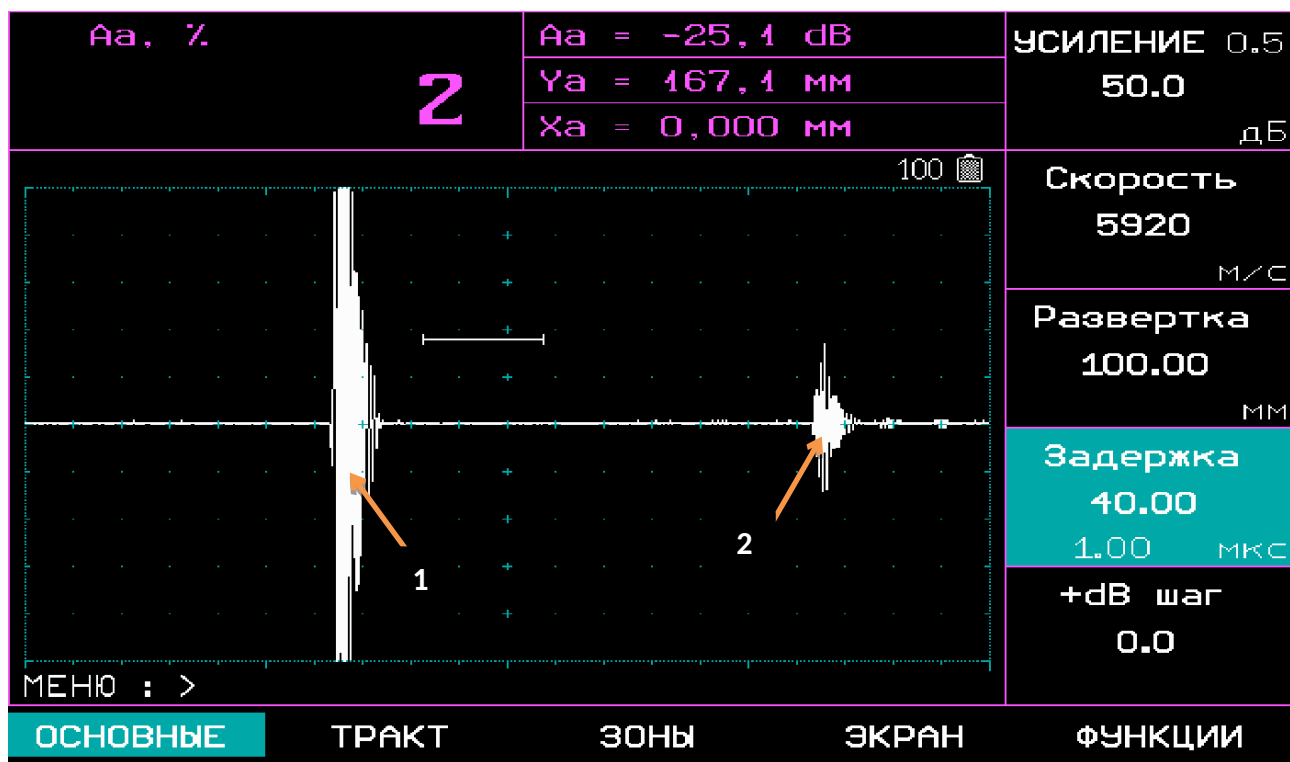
Участок калибровочного образца без отражателей (поз.
